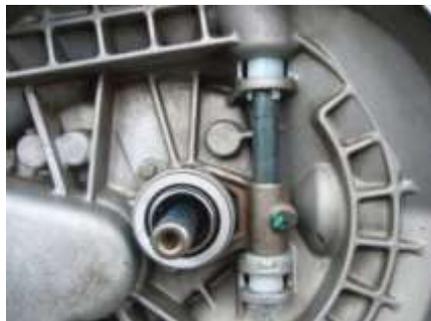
Montaje de Rodamiento, Horquilla, Palanca, canastas de Embrague
